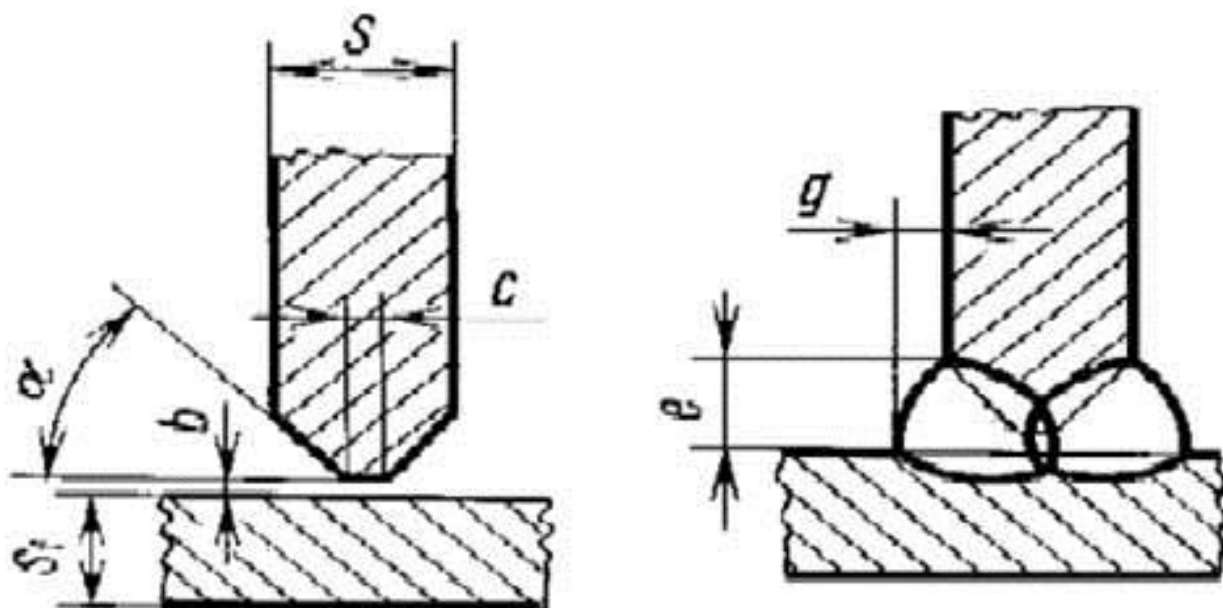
Конструктивные элементы разделки кромок и сварного соединения при сварке поясков и стенки
